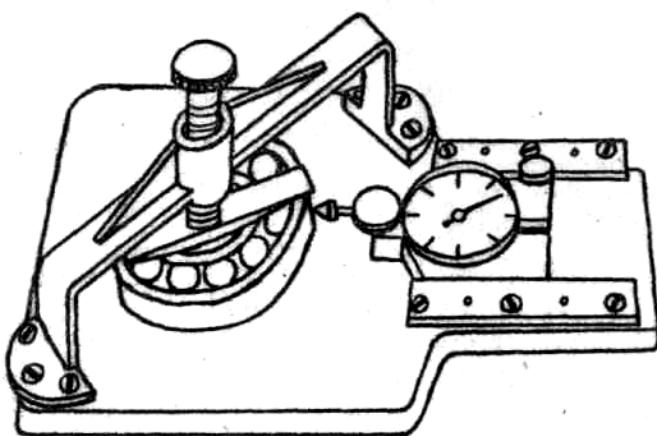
Прибор КИ-1223 для дефектации подшипников
